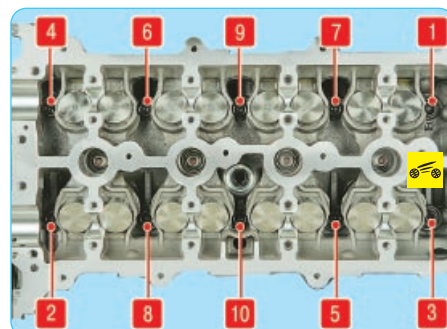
Порядок выворачивания болтов крепления головки блока цилиндров
